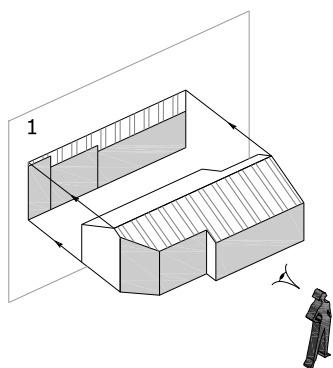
Vue de face (observateur situé face à l'objet, plan hôte situé derrière l'objet)
